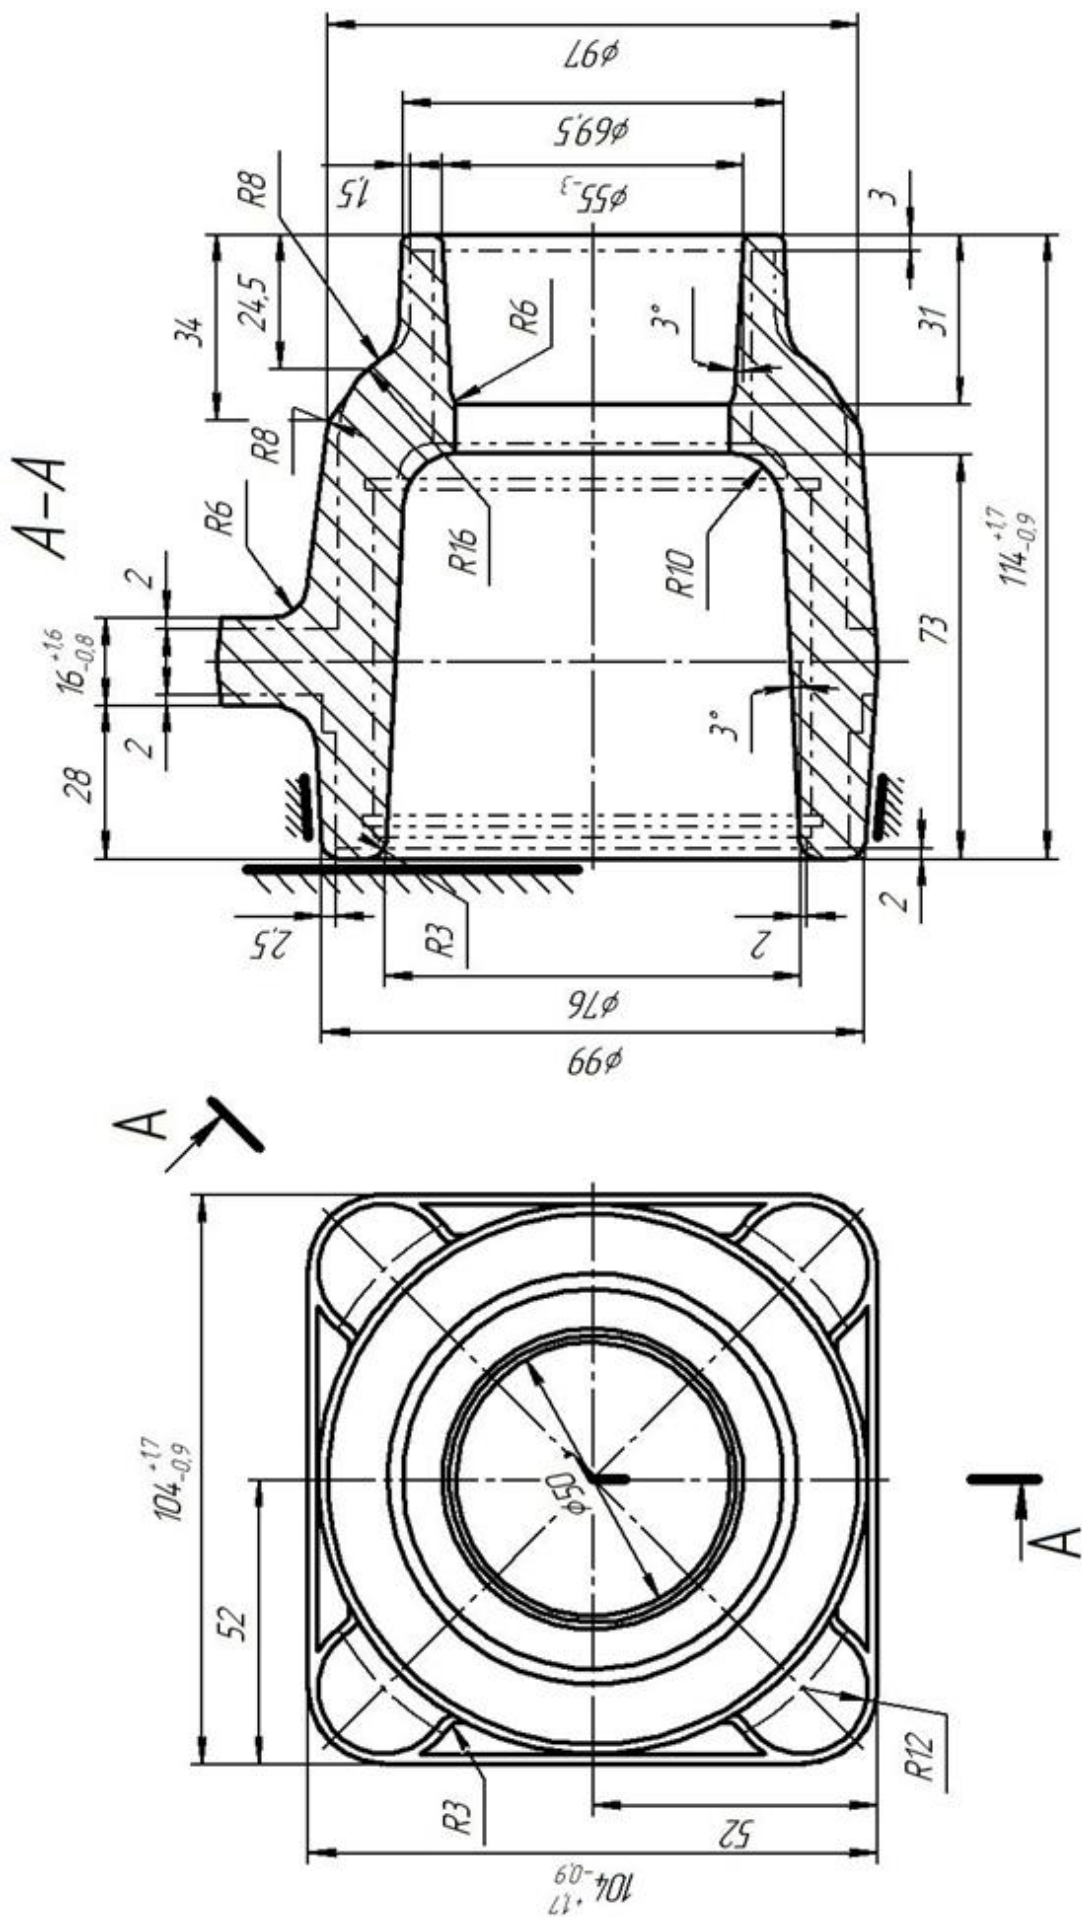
Приклад оформлення креслення штампованої поковки
